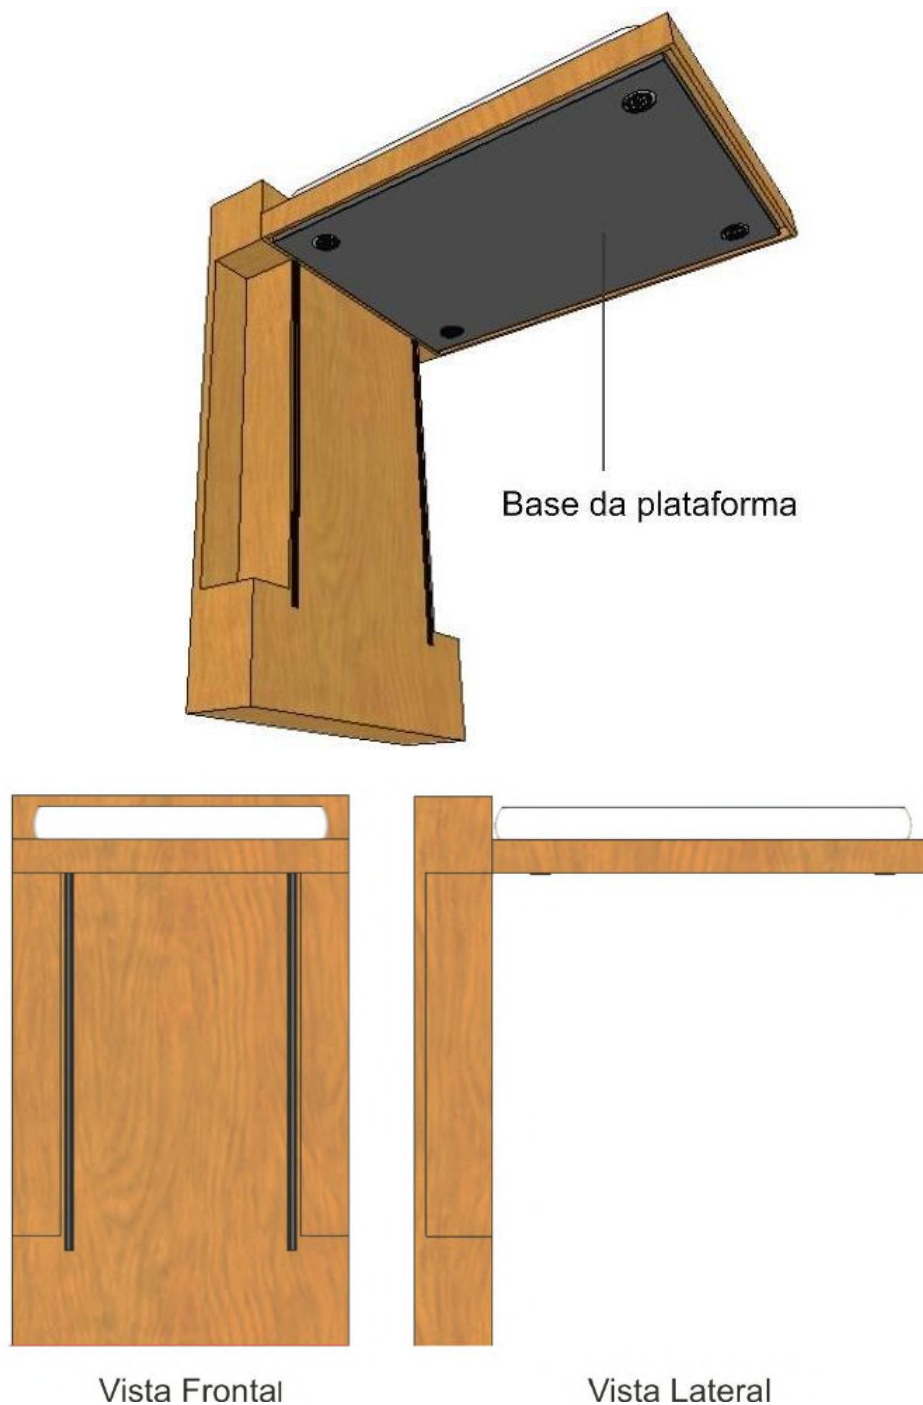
Detalhes explicativos da Alternativa B (Fonte: elaboração própria).
